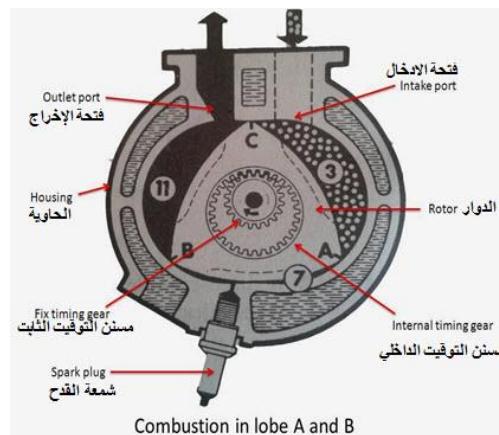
محرك Winkle وأجزاءه المختلفة
